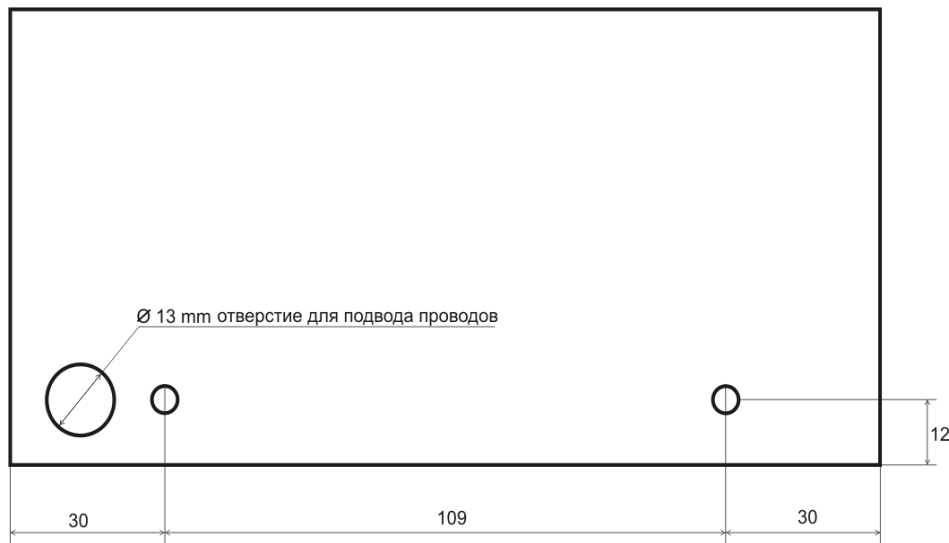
Установочный чертеж основания корпуса АБ-4.
